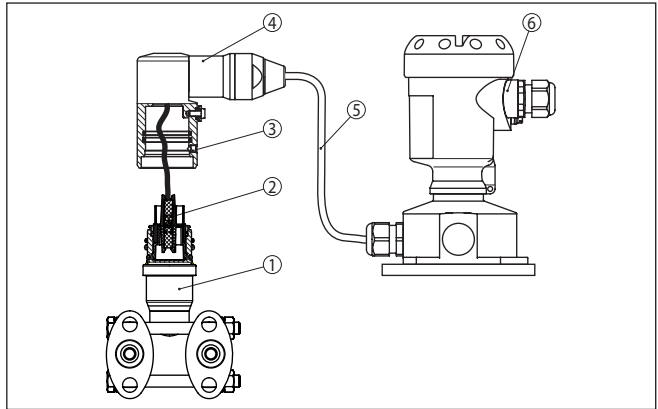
DPT-20 in IP68-Ausführung 25 bar und seitlichem Kabelabgang, externes Gehäuse
